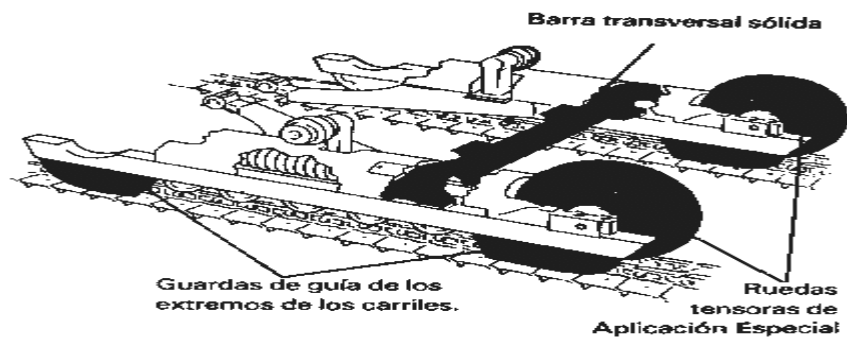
CARGADOR FRONTAL MONTADO SOBRE ORUGAS
